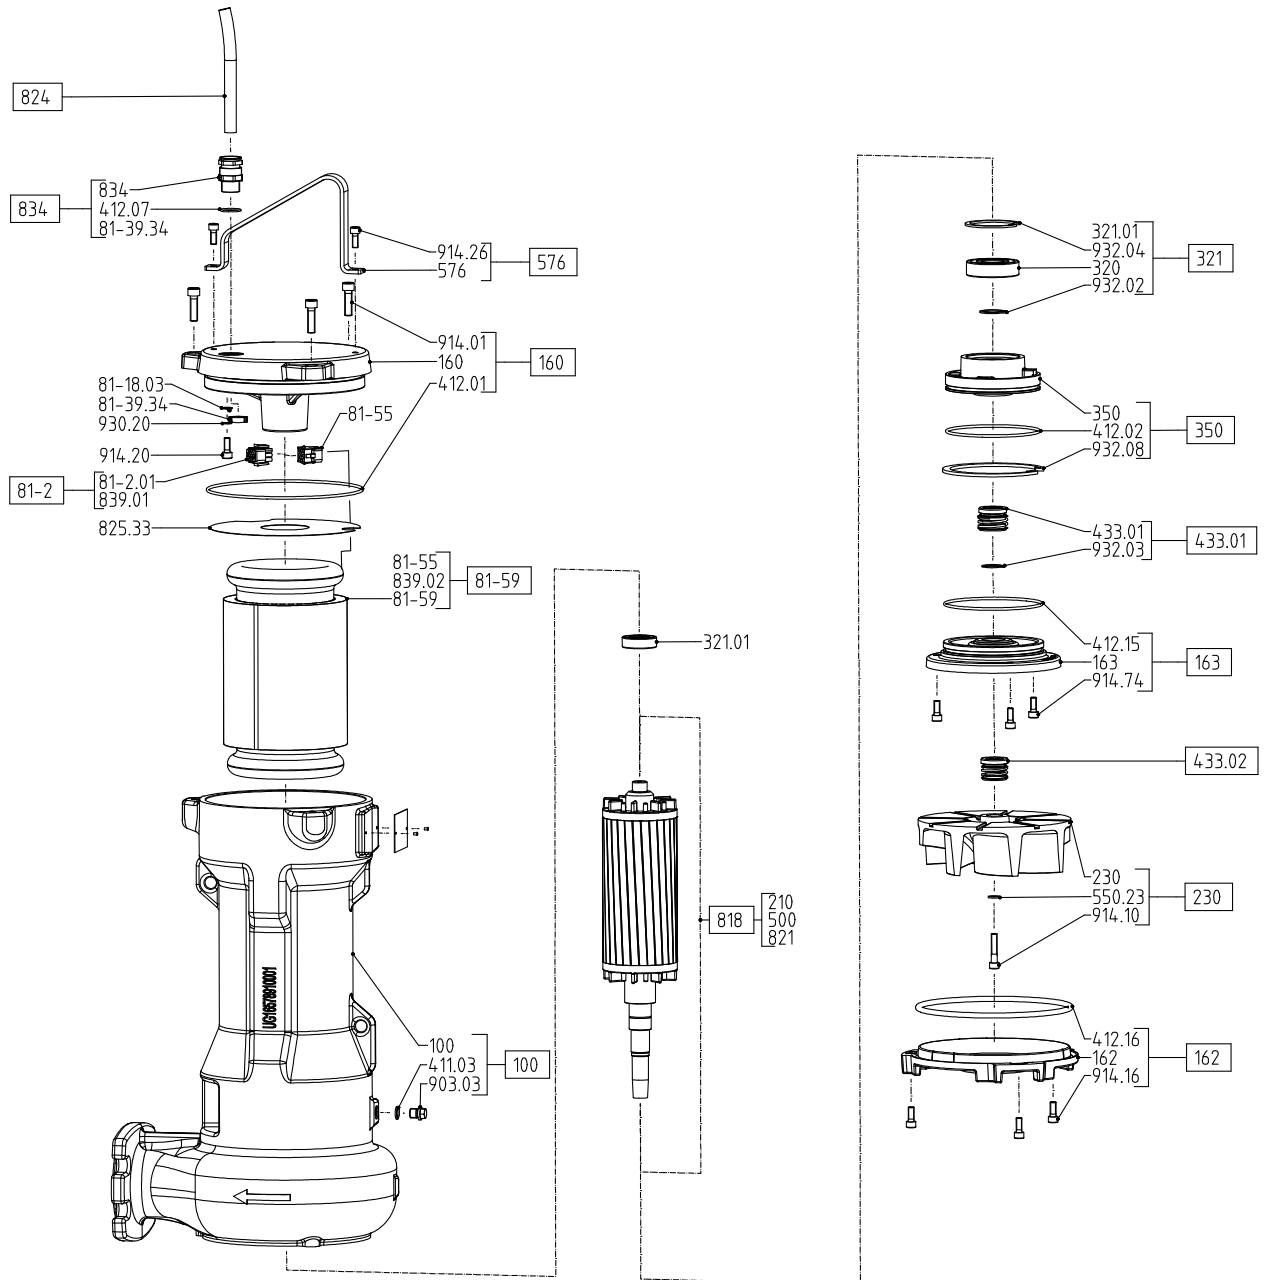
Explosionszeichnung Amarex F-max, Ausführung US
